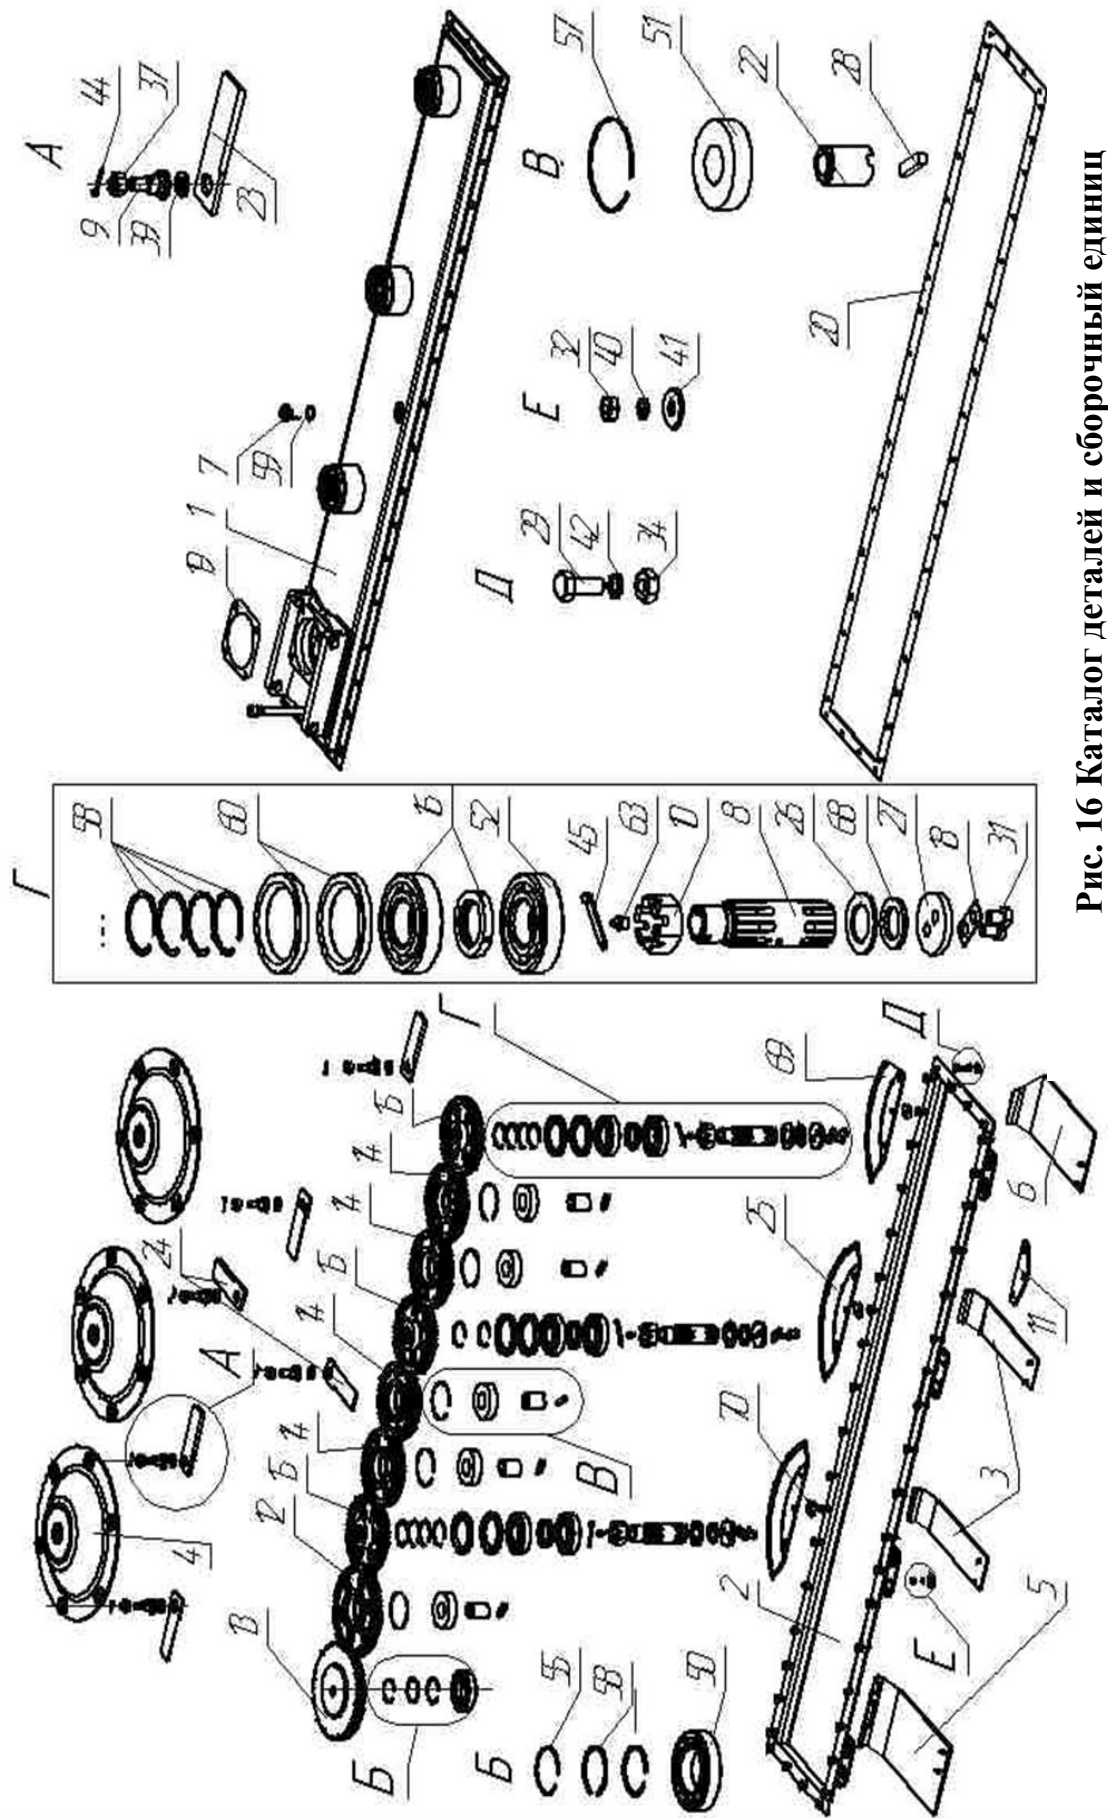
Каталог деталей и сборочный единиц аппарата режущего К-1.01.00.000.
